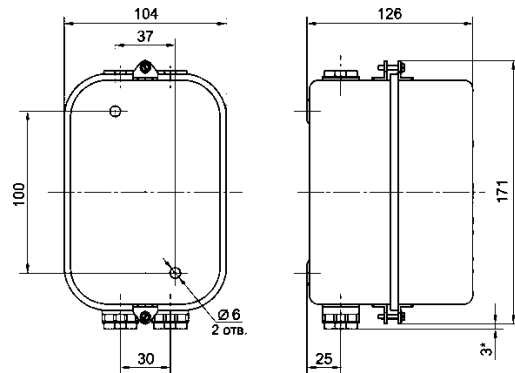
Пускатель ПМ12-010 10А в защитном корпусе - IP40; IP54
